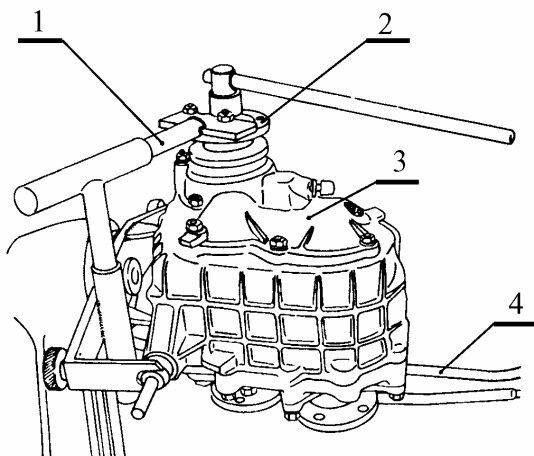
Установка раздаточной коробки на стенде Ач.22204:
